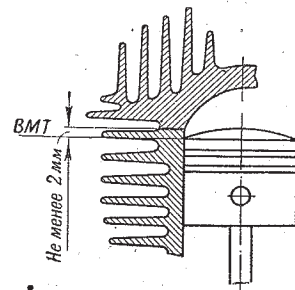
Минимальный зазор между кромкой поршня и головкой цилиндра
